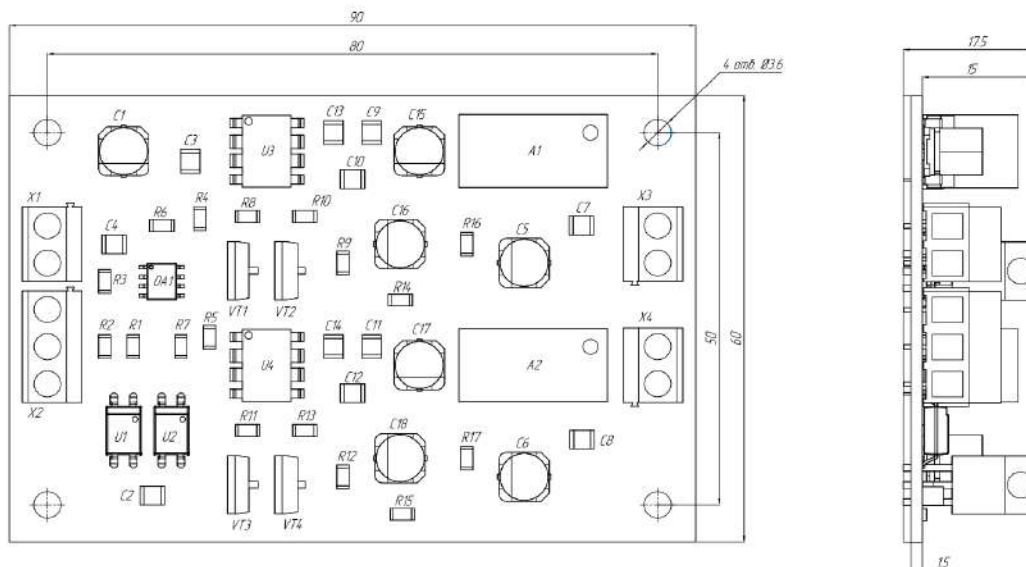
Сборочный чертеж печатного узла генератора управляющих импульсов
